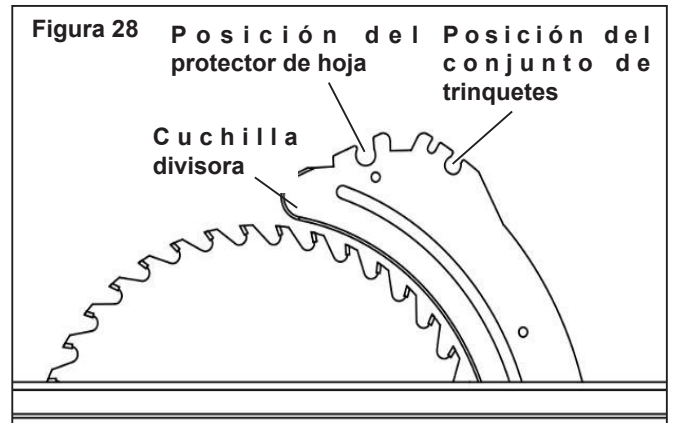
Posición del protector de hoja Posición del conjunto de trinquetes
